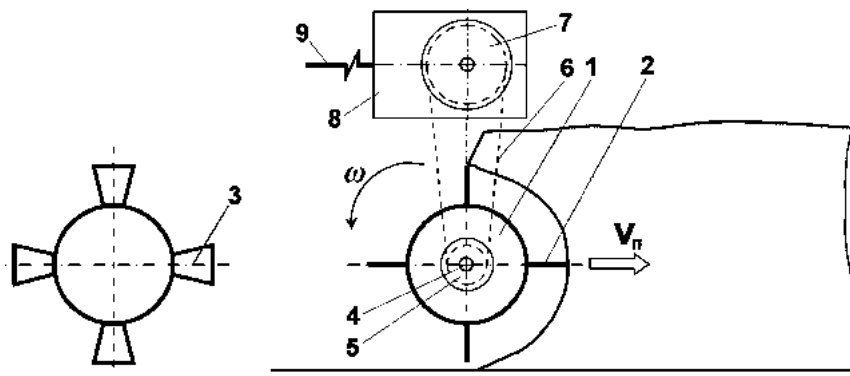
Схема установки: 1 – барабан; 2 – лопать пряма; 3 – лопать похила; 4 – вал барабана; 5 – зірочка ведена; 6 – ланцюгова передача; 7 – зірочка ведуча; 8 – редуктор конічний; 9 – ВВП трактора
